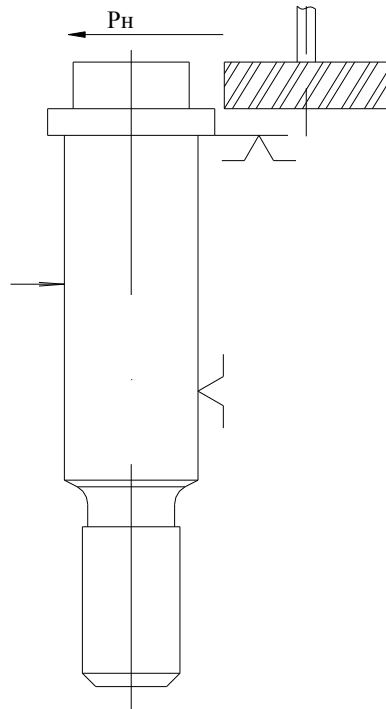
Розрахункова схема сил при шліфуванні в приспособленні
